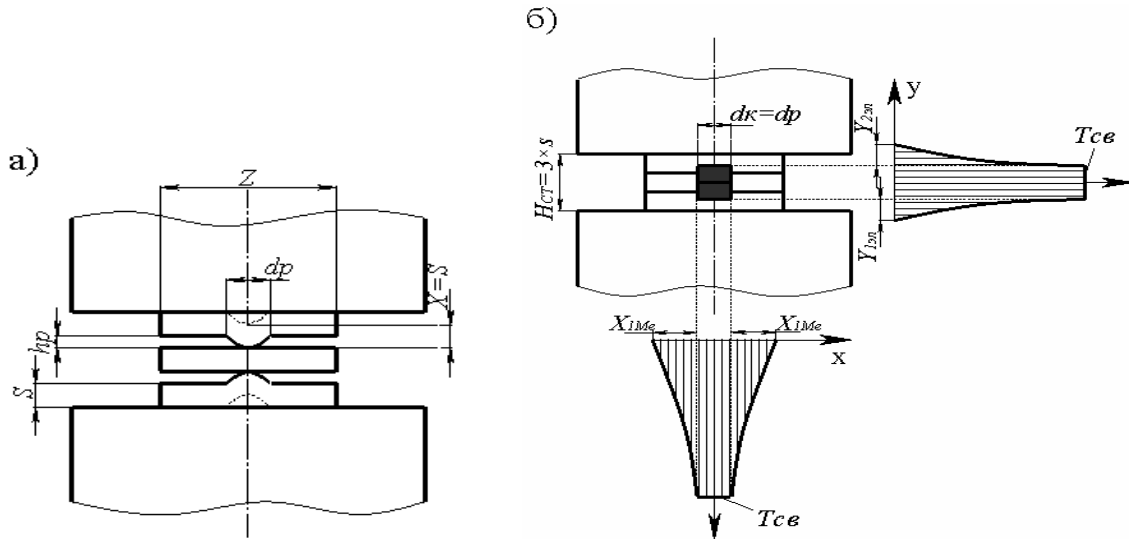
Расчетная схема сварного соединения: а – геометрия соединения перед сваркой; б – схема расчета теплового баланса деталей
